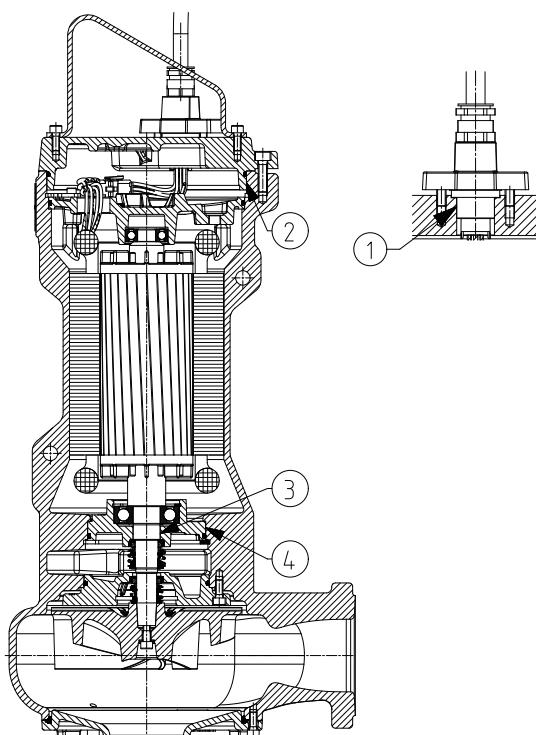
Обзор поверхностей взрывозащитных зазоров
